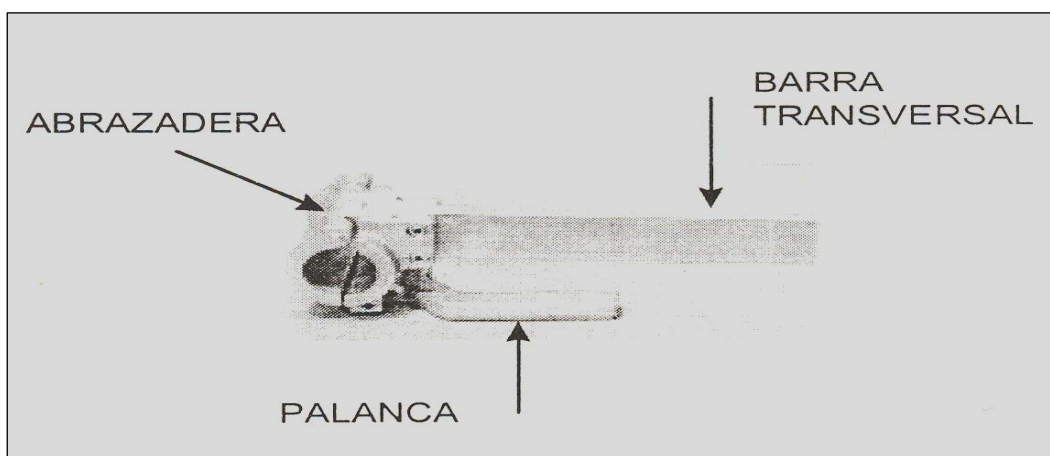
Barra Transversal y Accesorios Para Sujeción.
